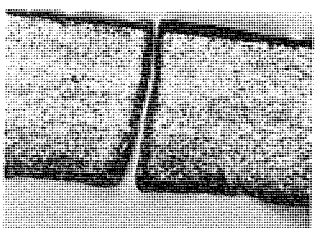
切断みぞの断面 (ステンレス鋼 厚さ 1 mm)
